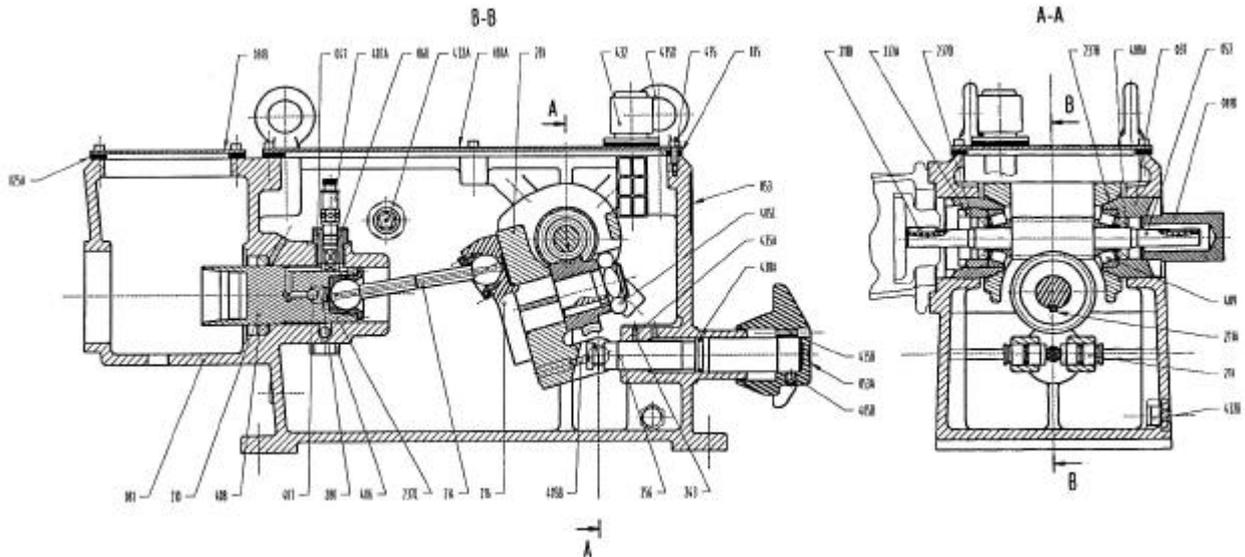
Extrait d'un exemple de plan d'ensemble industriel d'une pompe doseuse construite sur l'archétype du système bielle-manivelle à plateau incliné
